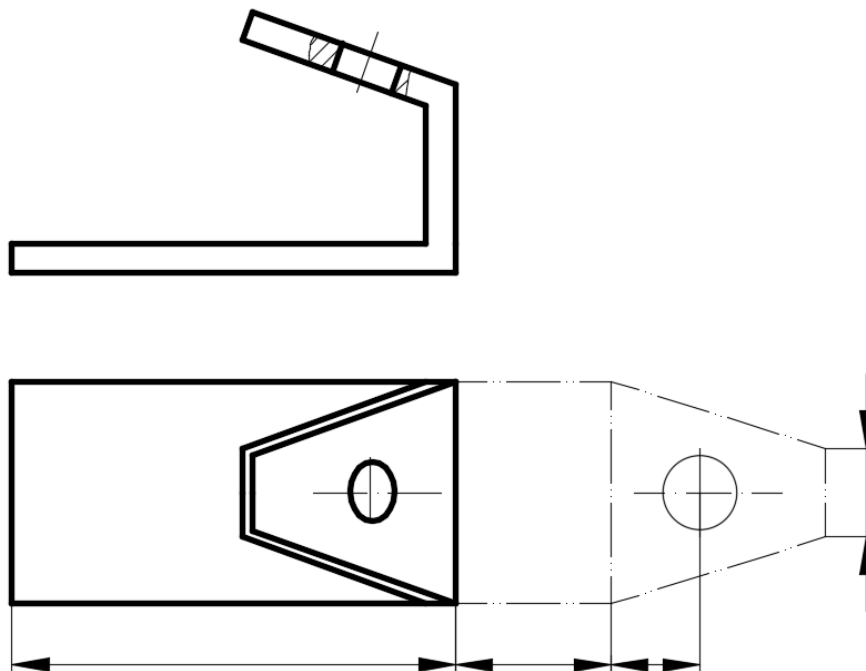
Образец выполнения чертежа детали, изготавливаемой гибкой.
